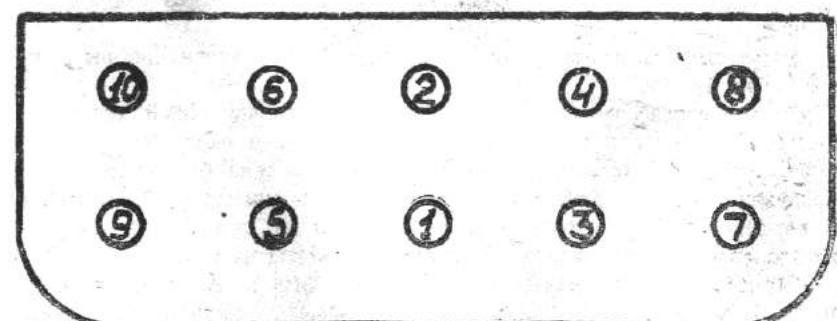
Порядок затяжки гаек головки блока цилиндров
